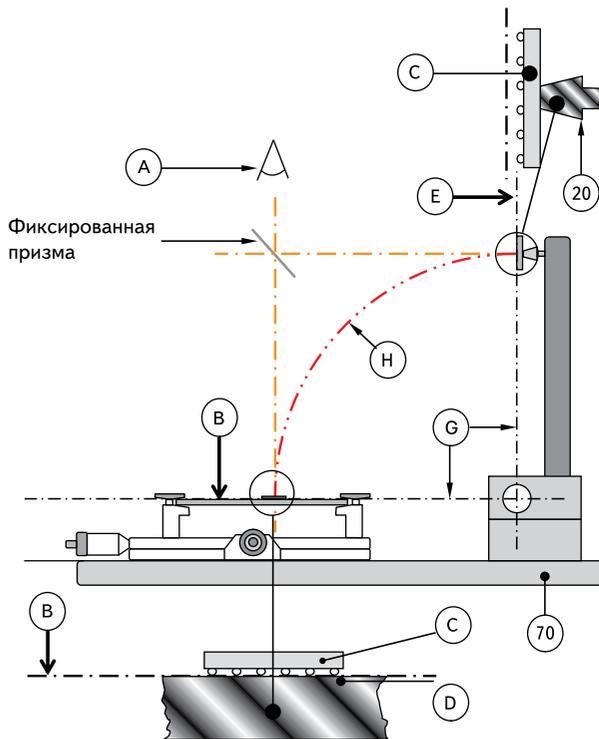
Схематическое изображение системы монтажа Finetech: A — точка обзора (микроскоп или камера); B — поверхность плат; C — микросхема; D — плата; E — верхнее положение модуля пайки; H — траектория движения модуля пайки; G — рабочие плоскости (B) и (E), образующие угол 90°
